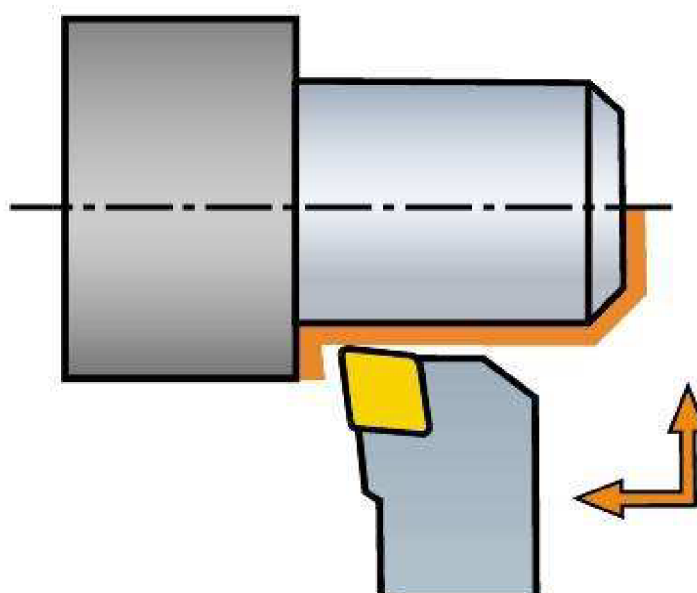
Soustružnický držák QS-3-80LR252531-10C [16].
